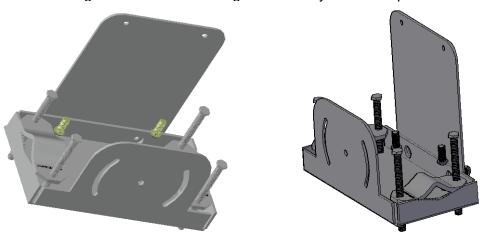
Kit de Montagem AP/Relay - Visões 3D
